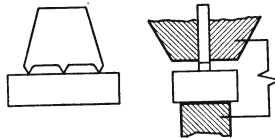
Gefräste Dachbuckel, z. B. hochkant Aufschweißen eines Bleches auf einen Klotz. Diese Buckel können auch gestanzt werden.
